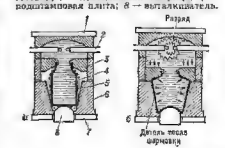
Схема электрогидравлической формовки: 1 — установка заготовки; 2 — конденсаторная батарея; 3 — катушка индуктивности; 4 — трубная заготовка; 5 — вытяжка изделия.
